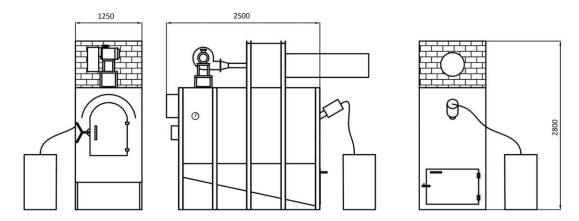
Габаритные размеры печи-инсинератора
